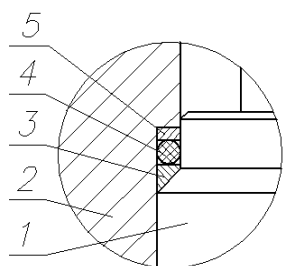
Схема уплотнения стержня в корпусе вискозиметра: 1 – стержень; 2 – корпус вискозиметра; 3 – медная прокладка; 4 – резиновое уплотнение; 5 – стальная шайба
